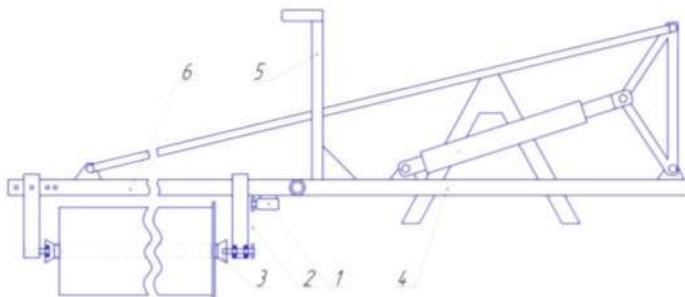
Приспособление для разматывания рулона укрывочного материала
